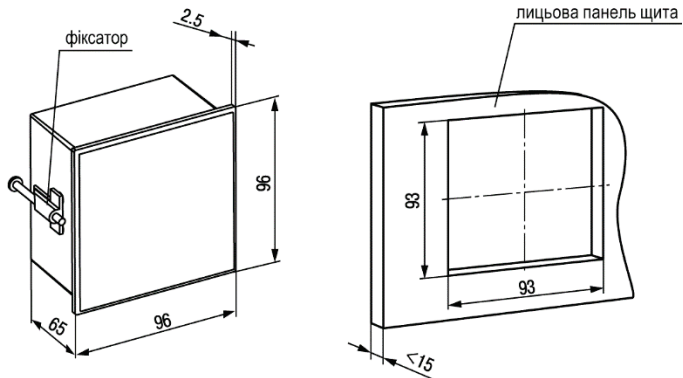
Габаритні розміри корпусу Щ1
